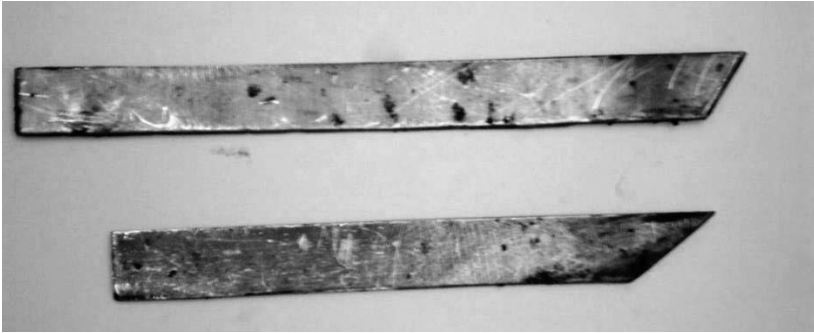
Пластини з термообробленої сталі 130Г7ТЛ підготовлені для пайки
